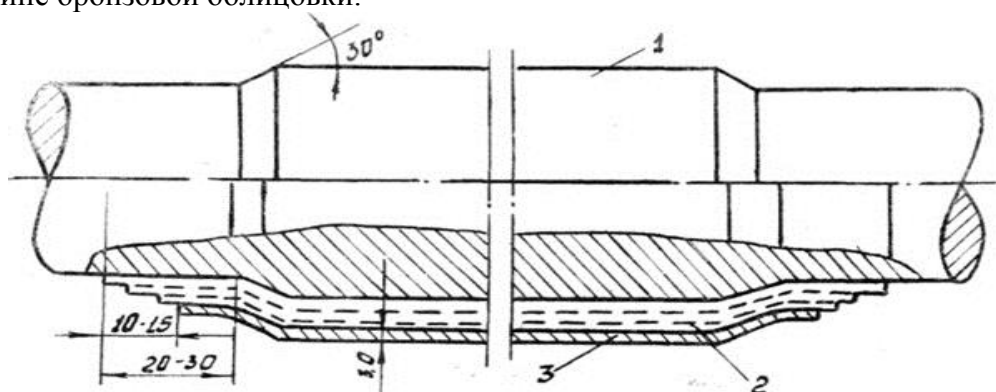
Конструктивный вариант ремонтной наплавки гребного вала с заменой бронзовой облицовки: 1 - гребной вал; 2 - подслоя, наплавленный порошковой проволокой ПП-Нп-07Х12НЗМ2Г2С; 3 – коррозионностойкий слой, наплавленный высоколегированной электродной проволокой или лентой.
